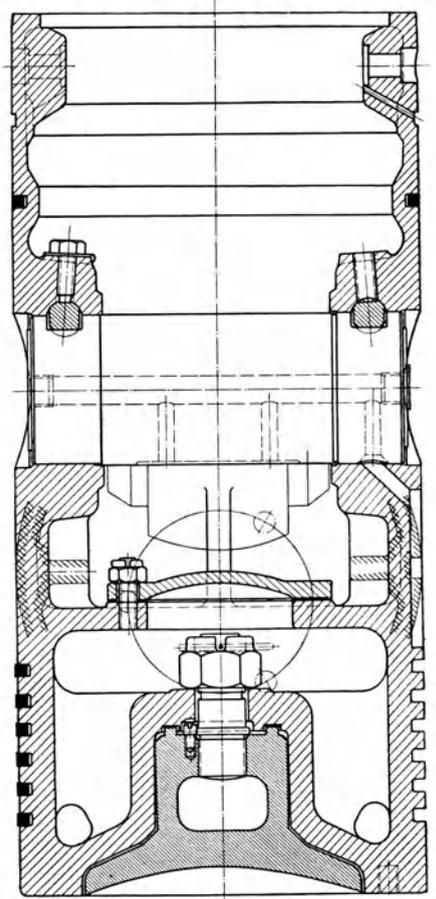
Kolben einer Dieselmachine. Zeigt außer dem Längsschnitt einen Schnitt senkrecht zur Bildebene (Horizontalschnitt) und die Angabe des Schraubenlochkreises.
